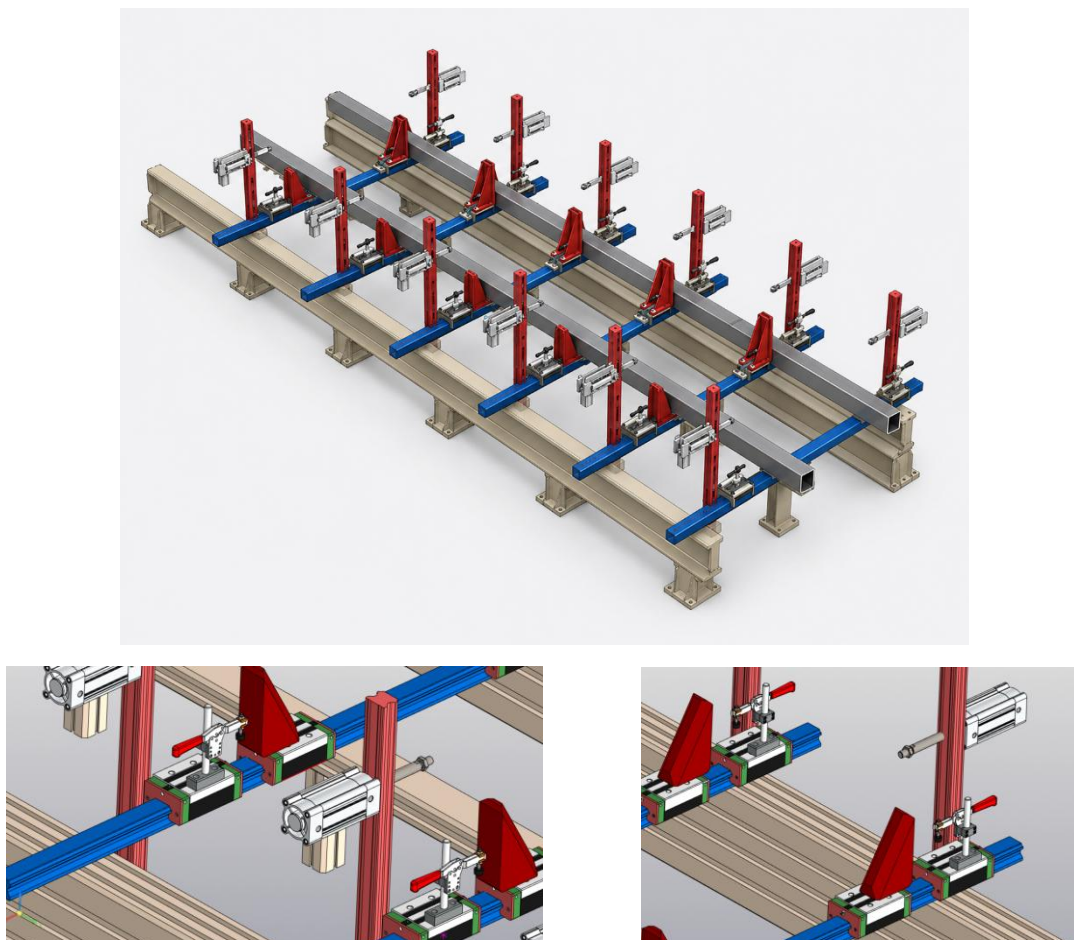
Складально-зварювальний кондуктор виготовлення вил
